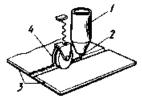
Схема экструзионной сварки пластмасс:
